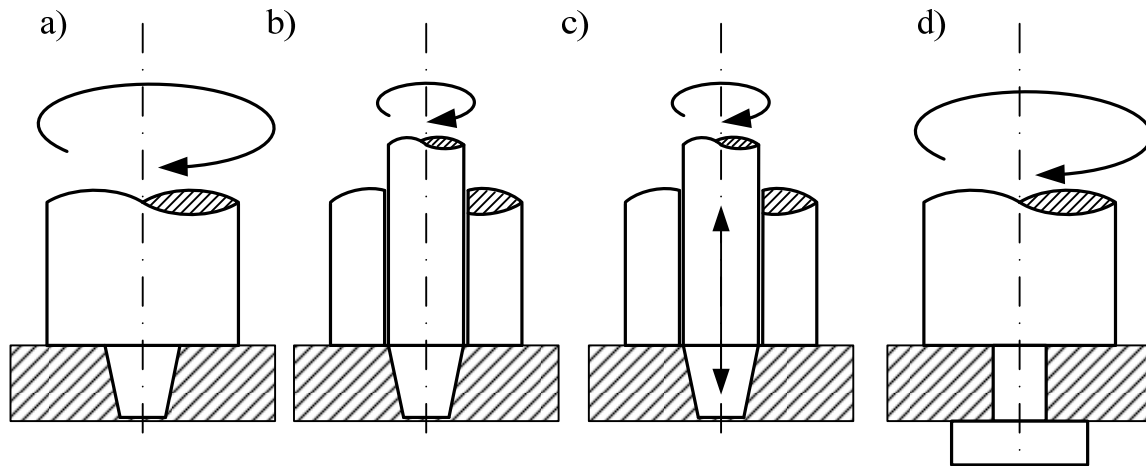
Unterschiedliche FSW-Werkzeugkonzepte: a) konventionelles Konzept; b) Werkzeug mit feststehender Schulter; c) Werkzeug mit variabler Pinlänge; d) Doppel-Schulter-Werkzeug
